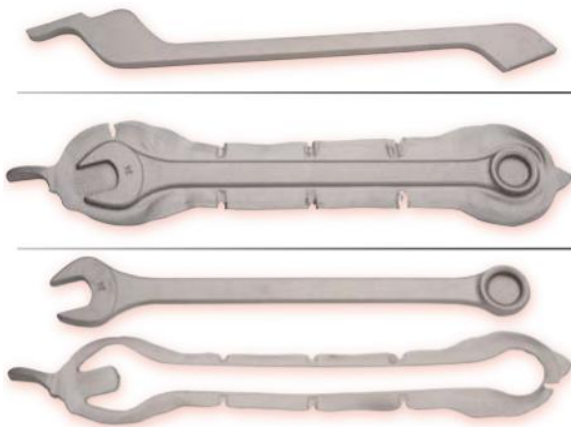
Изготовление поковок гаечного ключа фирмы UNIOR
